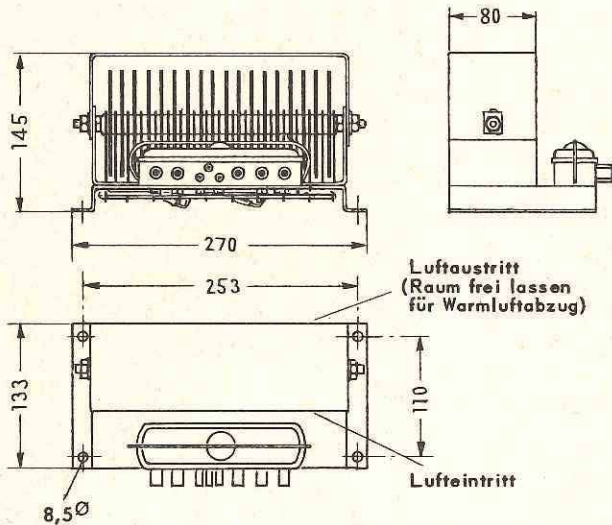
Die Abmessungen eines Selengleichrichters für 27A für einen Bosch-Drehstromgenerator von 1955.
